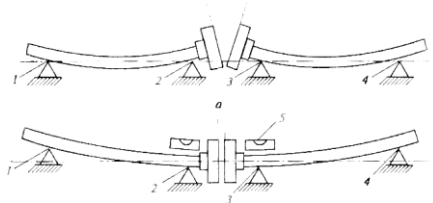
Положение валов, соединяемых с помощью полумуфт: а — до выверки; б — после выверки линии вала; 1...4 — подшипники; 5 — уровень
